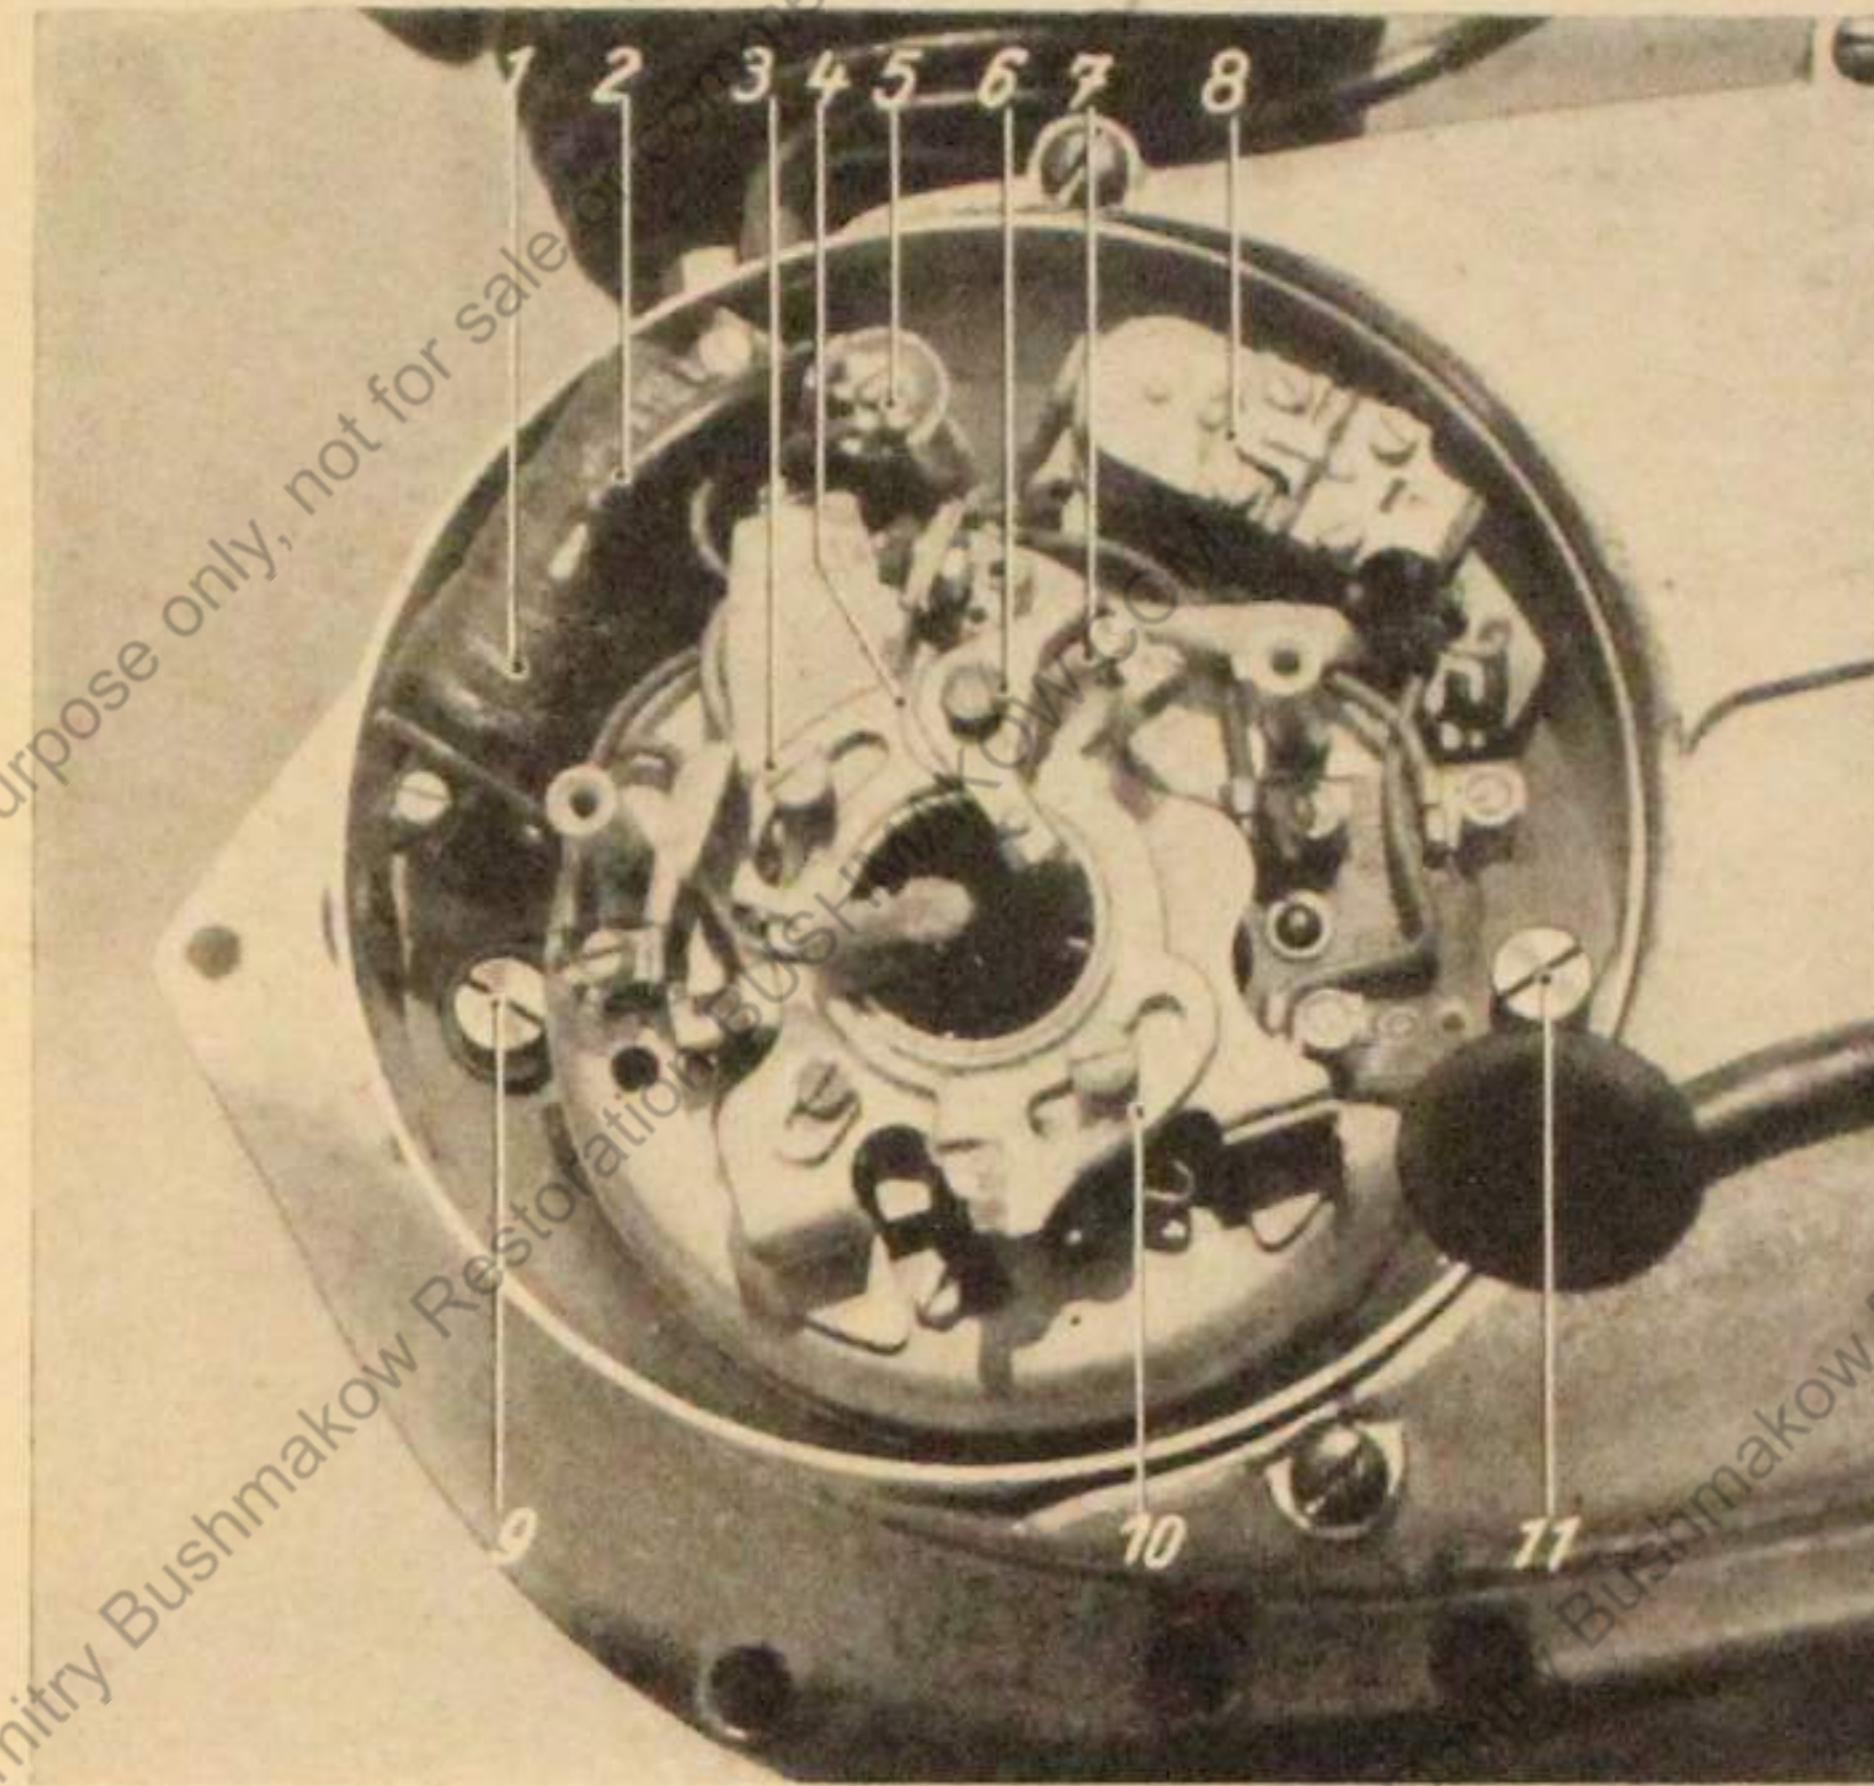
Lichtzündmaschine mit Unterbrecher und Zündspule, Draufsicht
